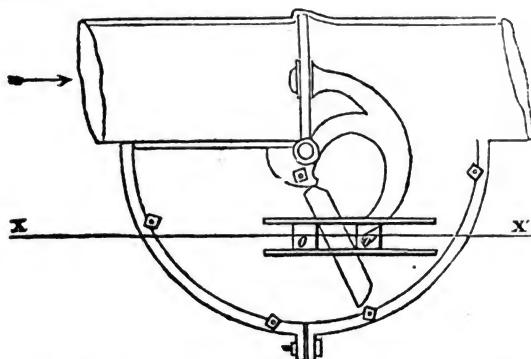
Vue de la soupape d'entrée dépouillée de son couvercle.
